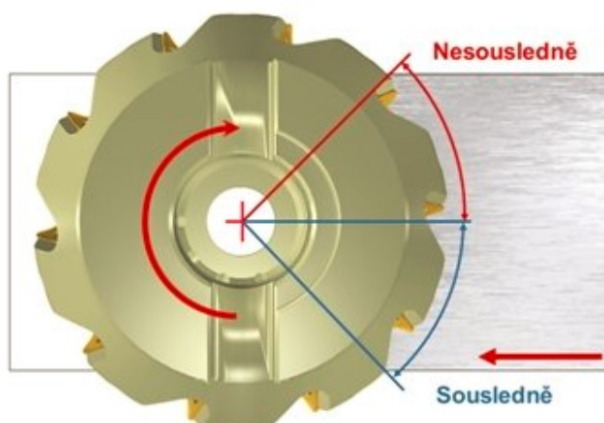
Sousledná strategie čelního frézování ¹⁹
